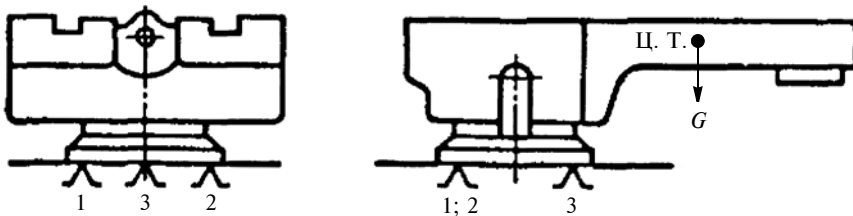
Базирование каретки револьверного суппорта станка плоскостью (1, 2, 3 — установочная база)
